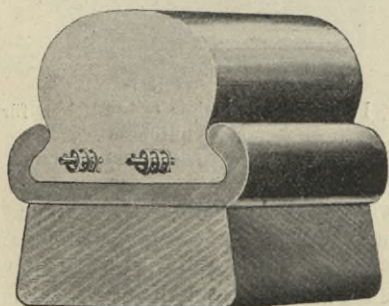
Carmontscher Befestigungsmodus durch Drähte, die mit Drahtspiralen umwickelt sind.
